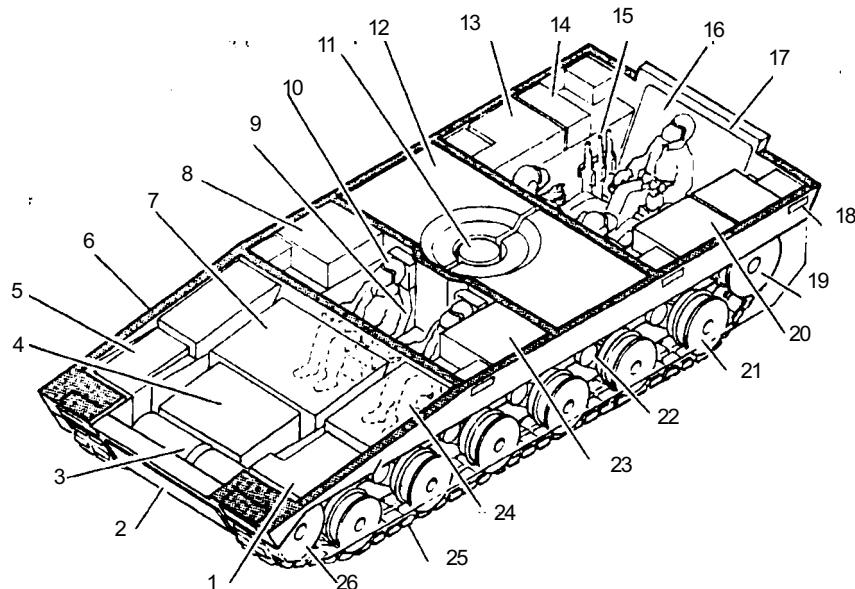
Вариант компоновочной схемы корпуса основного боевого танка FCS (США) в деталях:
